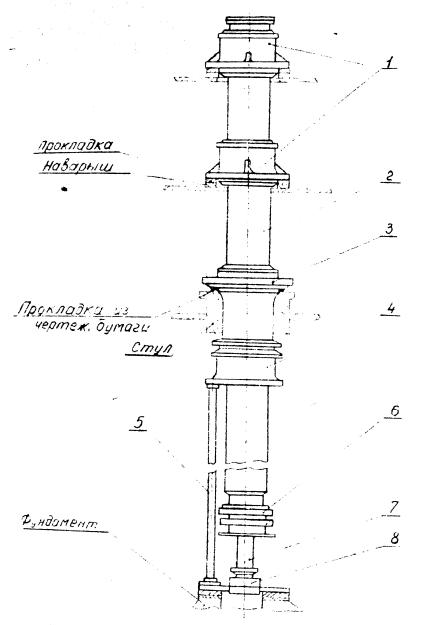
Рис. I Схема конструкции подъётно-мантового устройства неагрегатного исполнения
